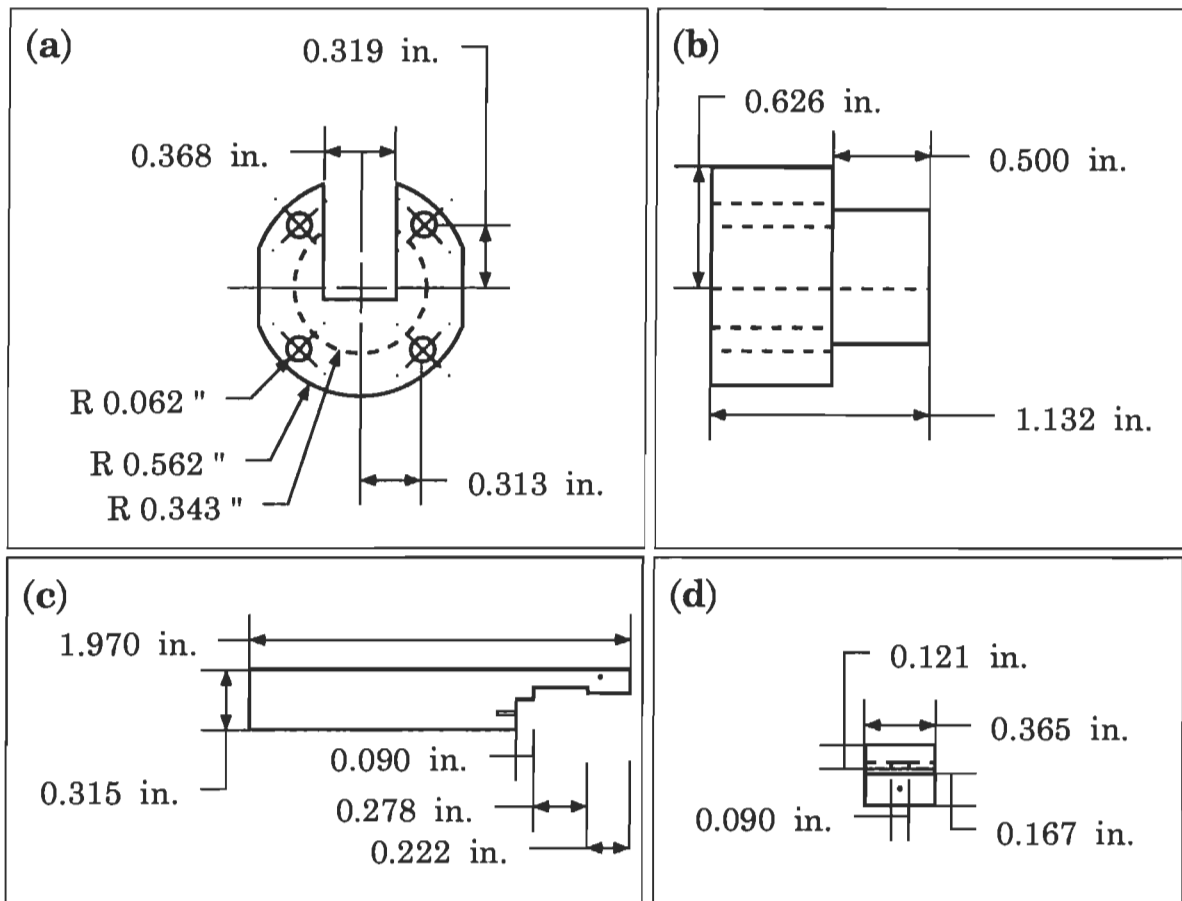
Vue de face [a] et vue de gauche [b] du guide du porte pointe.
